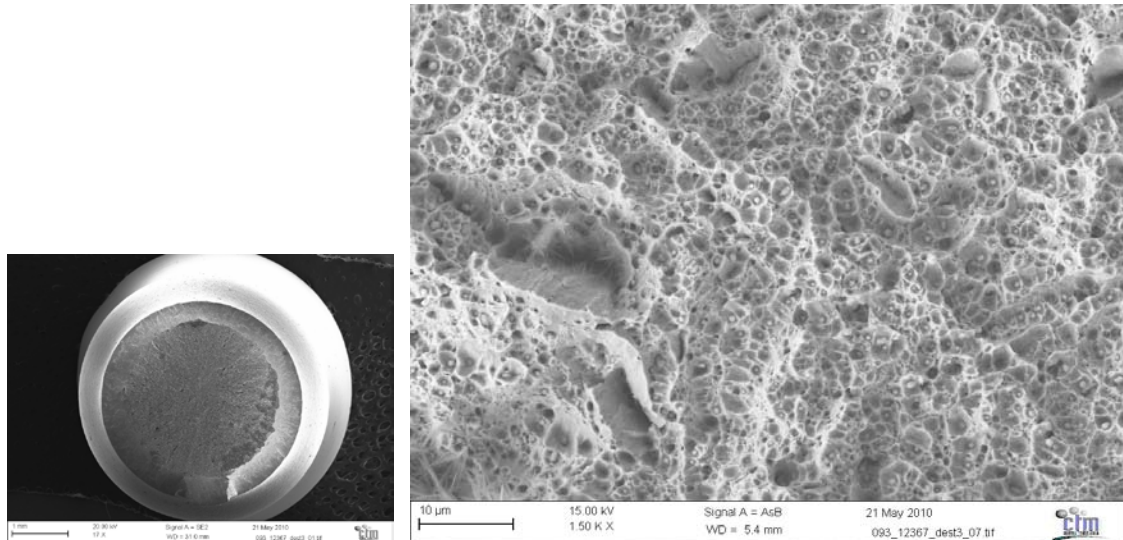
Superfície de fractura de la proveta de 1.2367 en aigua desionitzada a 40 °C.
